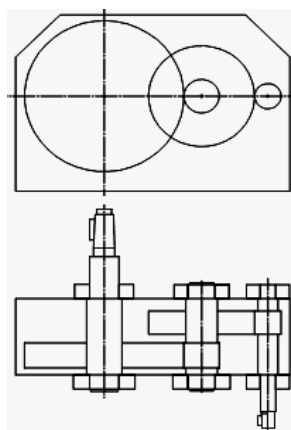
Эскизный проект цилиндрического двухступенчатого редуктора
